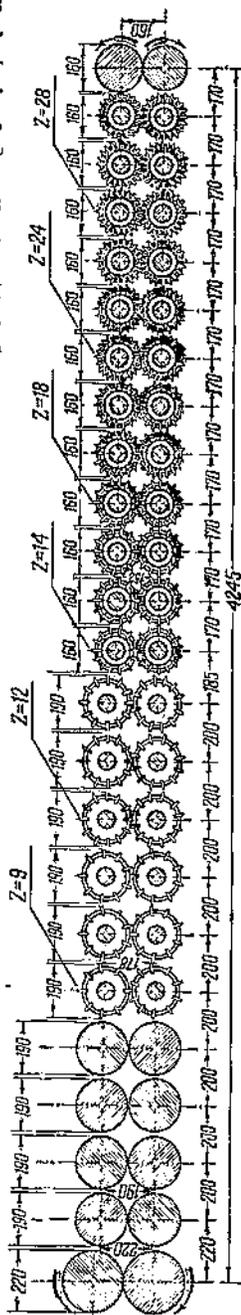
Схематический разрез ножевой мялки для конопли завода Фремса и Фреуденберга
